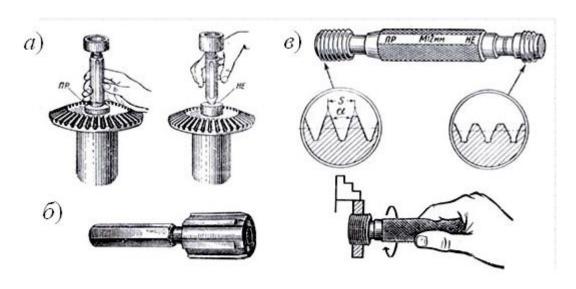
Общий вид калибров-пробок (a), шлицевой пробки (b) и резьбовой пробки (b)
